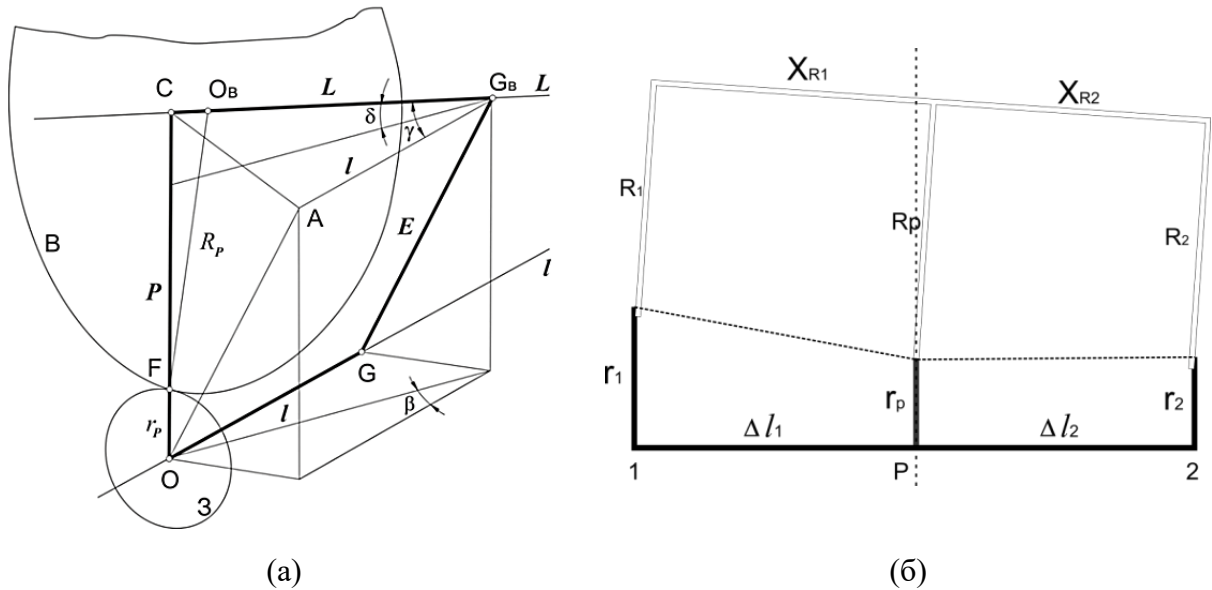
Схема взаимного расположения осей валка CL и прокатки Ol (а);
